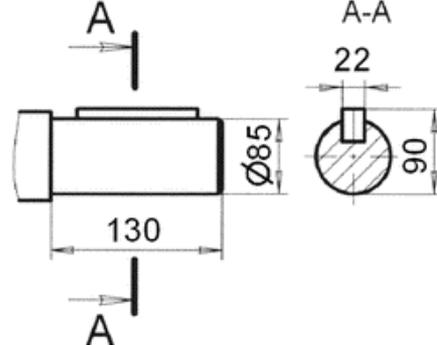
Размеры цилиндрического конца выходного вала редуктора 1ЦЗУ-250.
